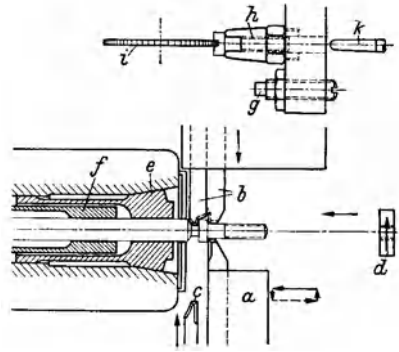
Bearbeitung einer längeren Kopfschraube.
